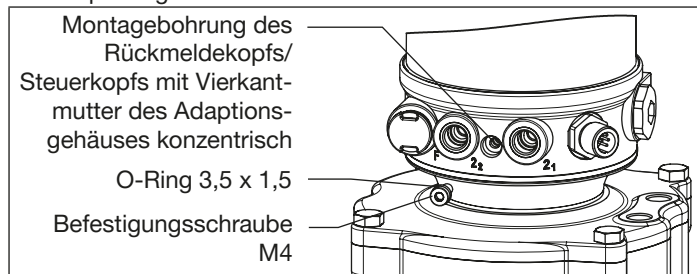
Befestigung Rückmeldekopf/Steuerkopf
